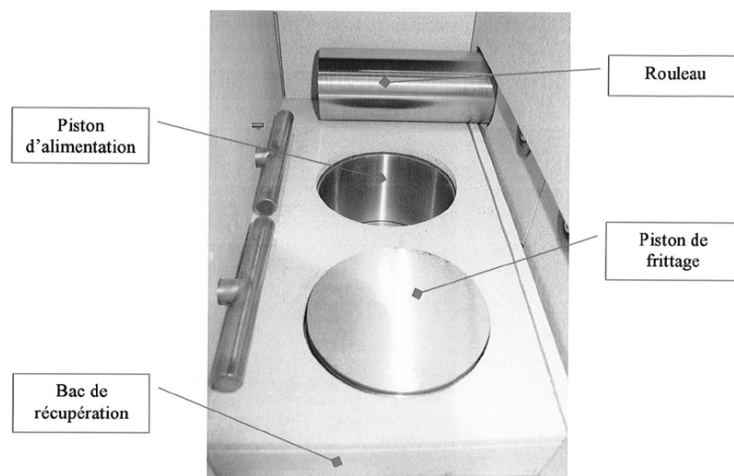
Chambre de fabrication de la machine Phenix PM100
